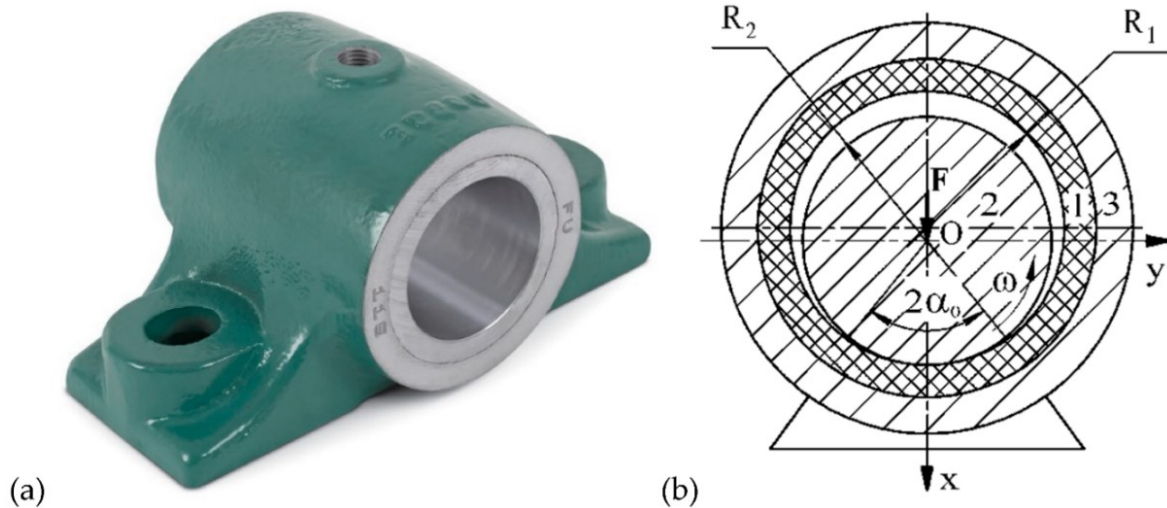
Загальний вигляд підшипникового вузла ковзання та розрахункова схема контактної взаємодії вала з полімерним покриттям [13]: (а) загальний вигляд корпусного підшипникового вузла ковзання з втулкою; (б) розрахункова схема контакту вала з полімерним покриттям підшипника ( $R_1$  – зовнішній радіус втулки;  $R_2$  – внутрішній радіус втулки;  $O$  – центр вала;  $F$  – радіальне навантаження;  $\omega$  – кутова швидкість обертання вала; 1 – металева втулка; 2 – вал; 3 – полімерне покриття)
